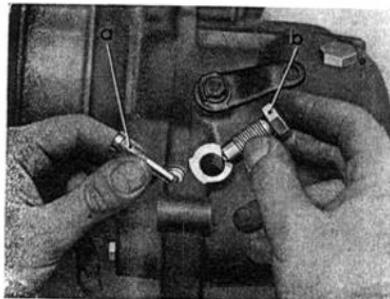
a = Arretierschraube für Anwerfvorrichtung (darf nicht verbogen sein!), b = Schaltarretierbolzen (mit Druckkugel), gleichzeitig Einfüllverschraubung für Getriebschmiermittel
